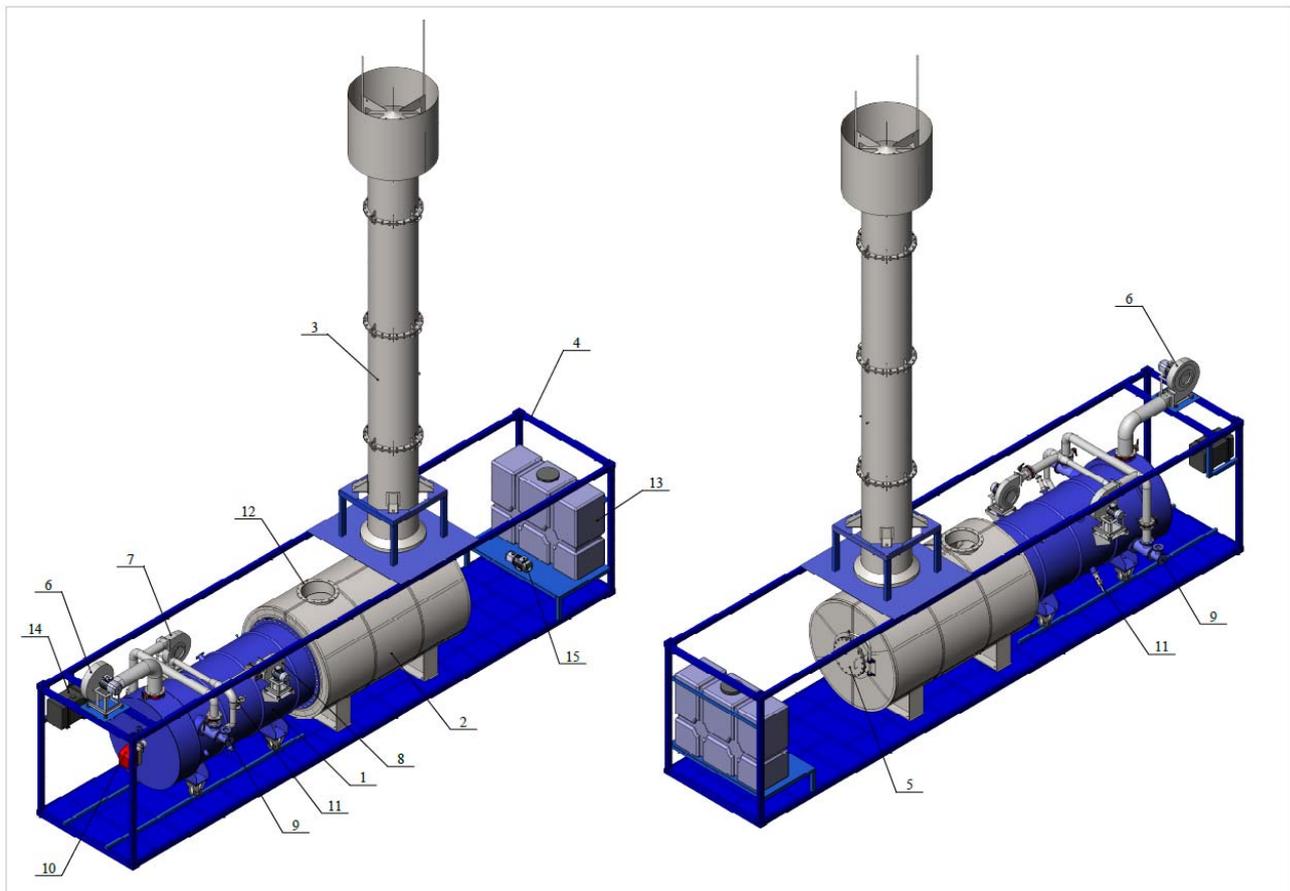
Общий вид Установки. 1 – Реактор обезвреживания биогаза; 2-Камера охлаждения дымовых газов; 3-Дымовая труба; 4-Блок-контейнер установки; 5-Люк обслуживания; 6-Центробежный вентилятор охлаждения дымовых газов; 7-Центробежный вентилятор первичного воздуха; 8-Центробежный вентилятор вторичного воздуха; 9-Горелочное устройство биогаза; 10-Горелочное устройство дополнительного топлива; 11-Форсунки подачи воды (пермеата); 12-Взрывной клапан; 13-Ёмкость воды (пермеата); 14-Топливный бак и узел подачи дополнительного топлива; 15-Насос подачи воды (пермеата)
